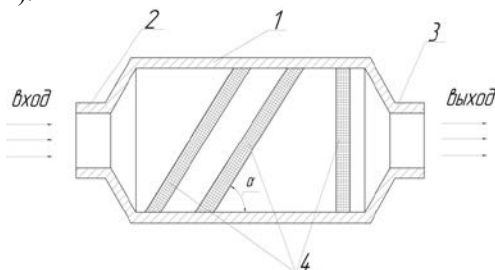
Сетчатый искрогасителя: 1 – корпус; 2 – подводящий патрубок; 3 – отводящий патрубок; 4 – пакет газораспределительного аппарата, установленный под углом  $\alpha = 55-65^\circ$
